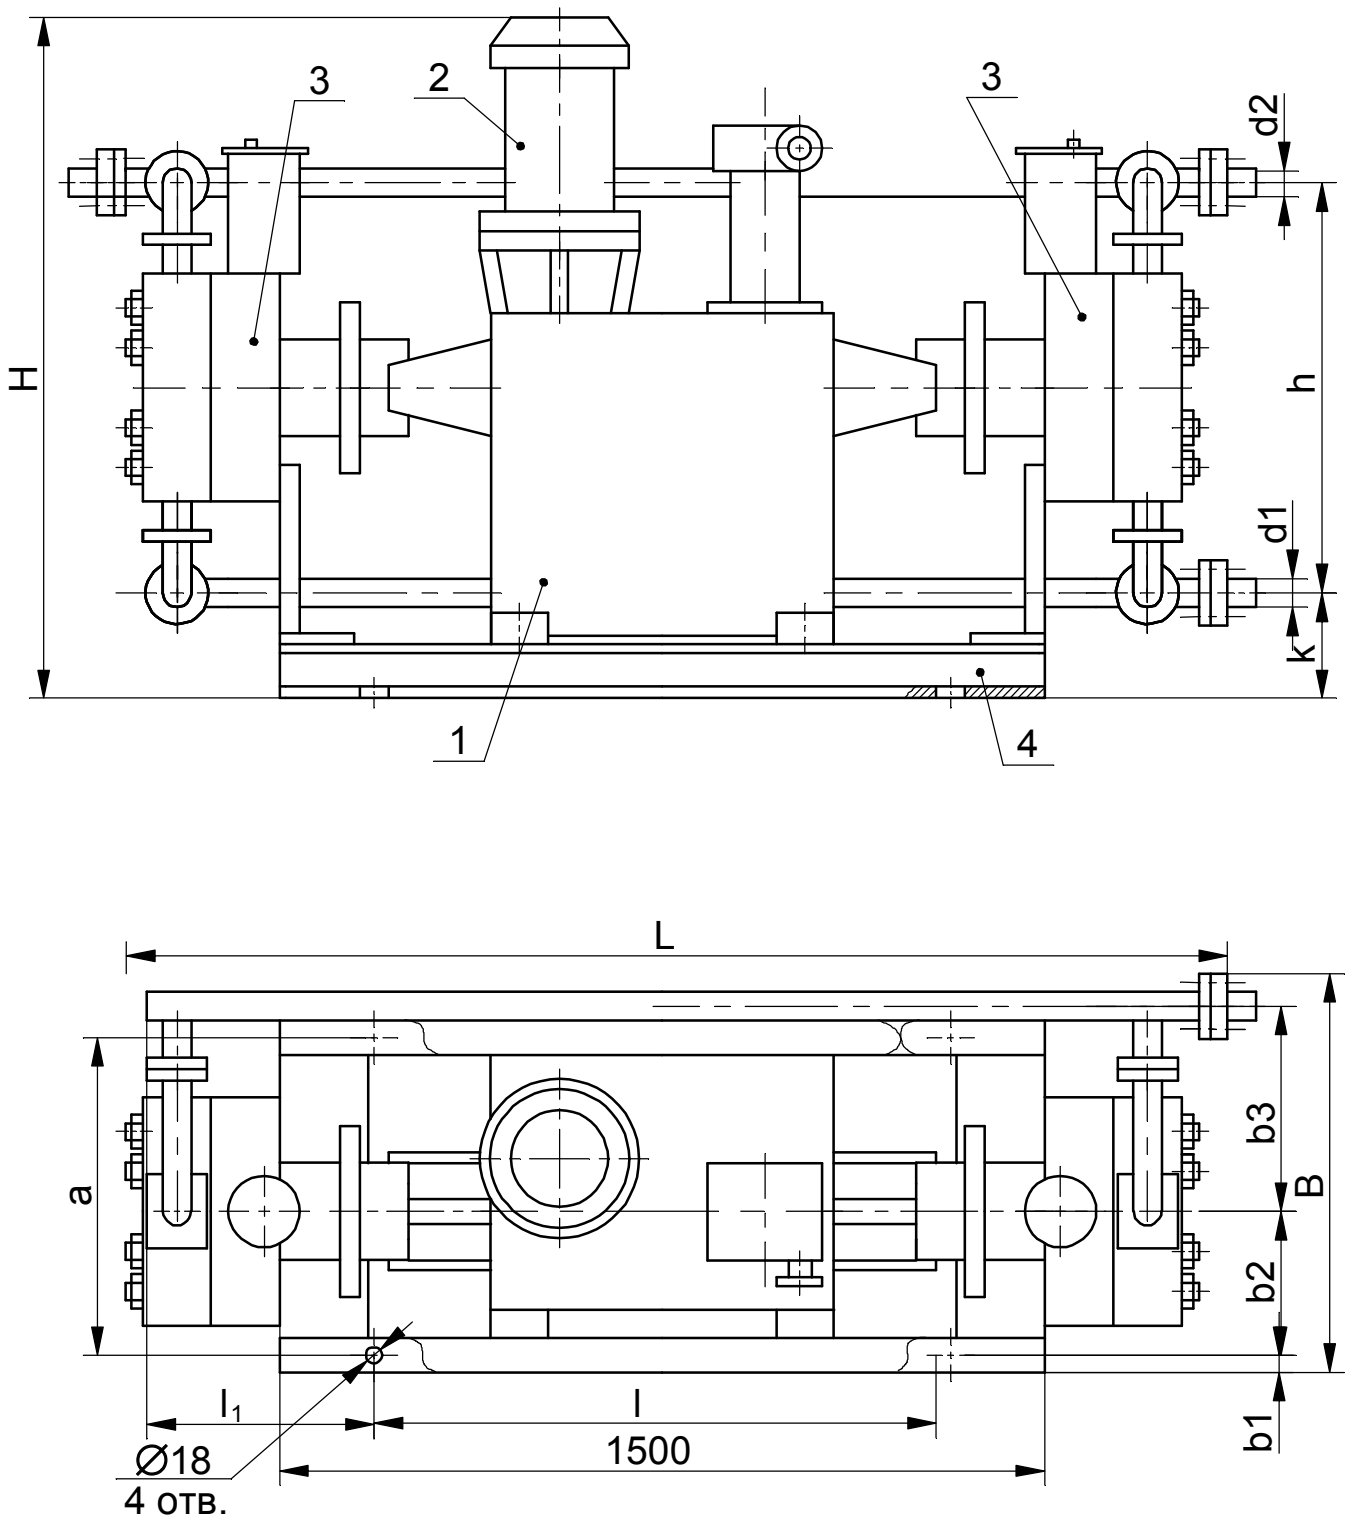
Внешний вид агрегата с параметрами номинального режима 1000/100; 1600/63; 2500/40; 4000/25 и 6400/16. Габаритные и установочные размеры
